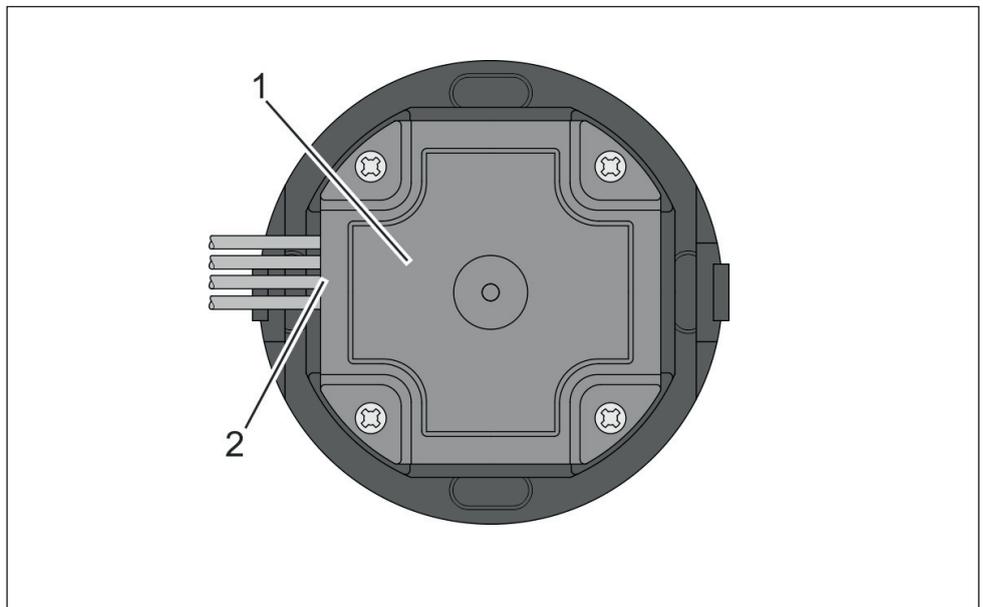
Vue arrière du WT 210 / WT 210 BLE avec câble
